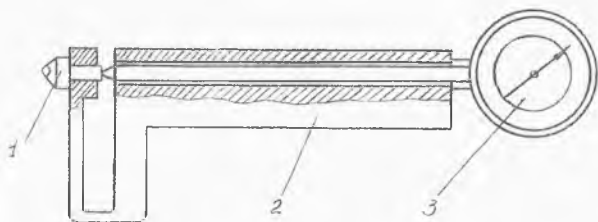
Пружинящая оправка для алмазного выглаживания наружных цилиндрических поверхностей: 1 — выглаживатель; 2 — корпус оправки; 3 — индикатор
